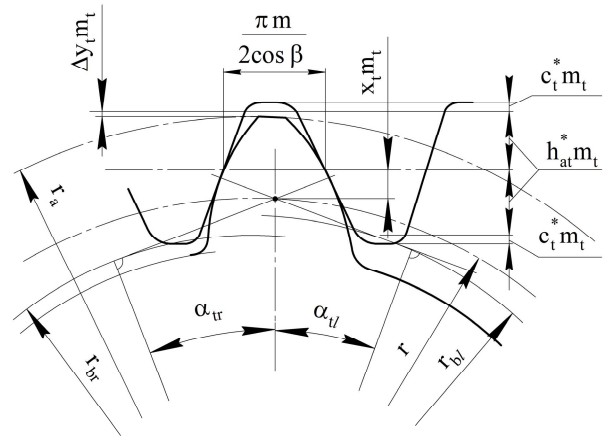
Торцовое сечение станочного зацепления ЭКК с производящей рейкой
